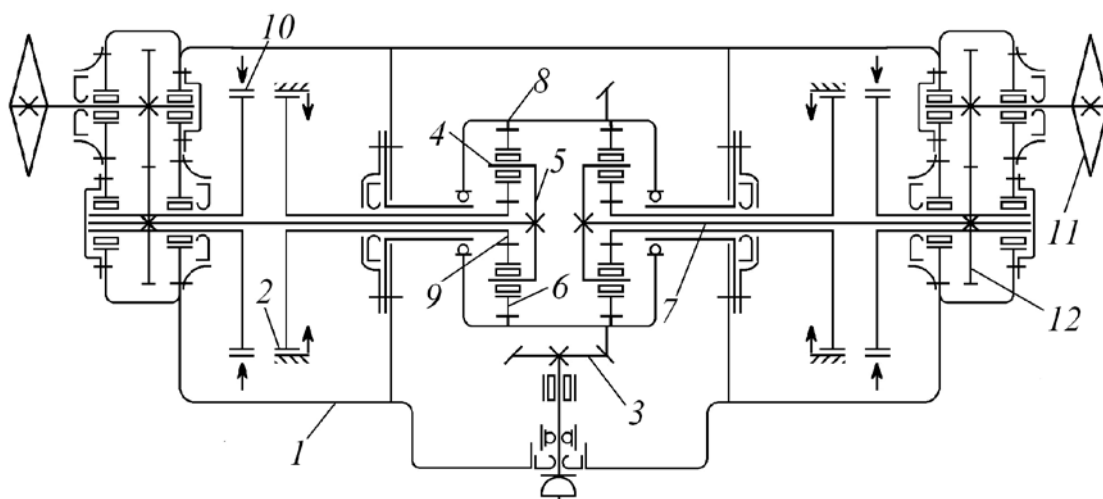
Сдвоенный планетарный механизм поворота:
